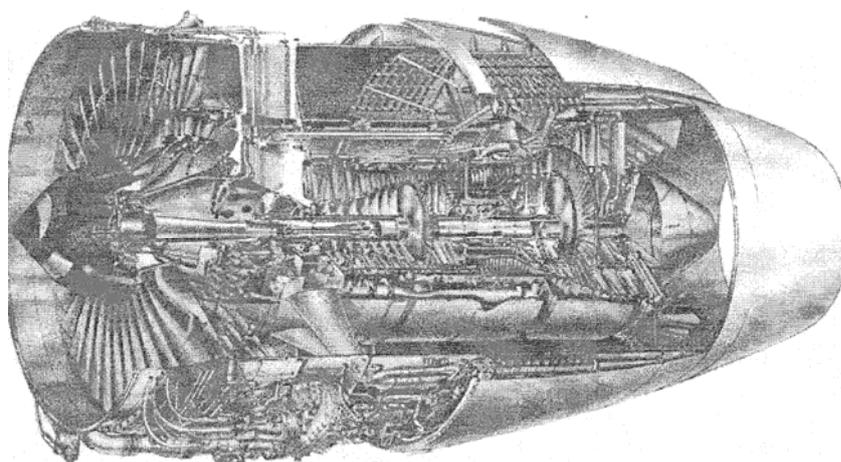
Двухконтурный турбореактивный двигатель пассажирского лайнера с турбовентилятором и осевым компрессором
